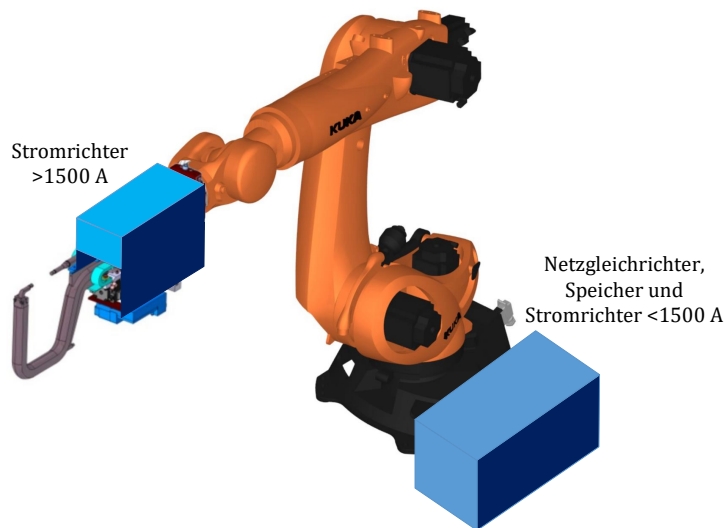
Beispielhafter Aufbau eines Schweißsystems. Die optimalen Positionen für die elektrischen Komponenten und den Speicher sind blau dargestellt. Der SMS kann nicht auf dem Roboterarm befestigt werden. Alle Hochstrom-Komponenten ($I \geq 1500 \text{ A}$) müssen sich an der Zange befinden.
